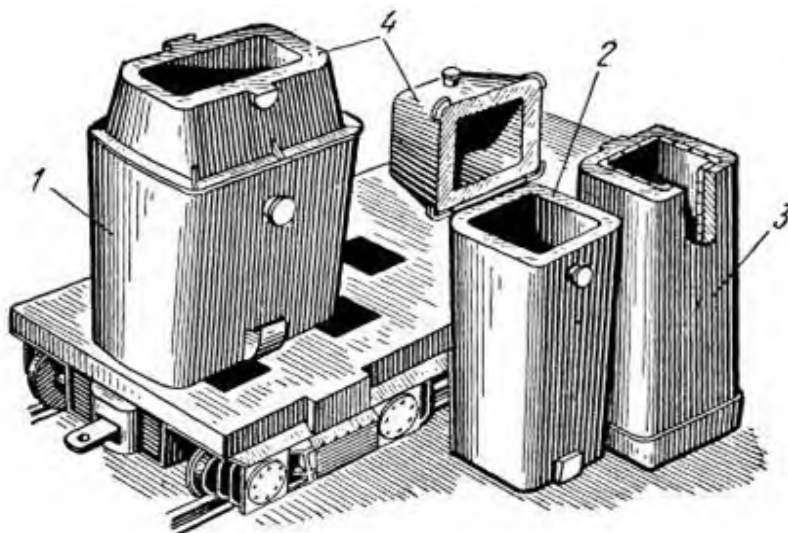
Виливниці для розливки спокійної сталі: 1 – для спокійного листового металу; 2 – розширена догори; 3 – з футерованим верхом; 4 – прибуткова надставка
